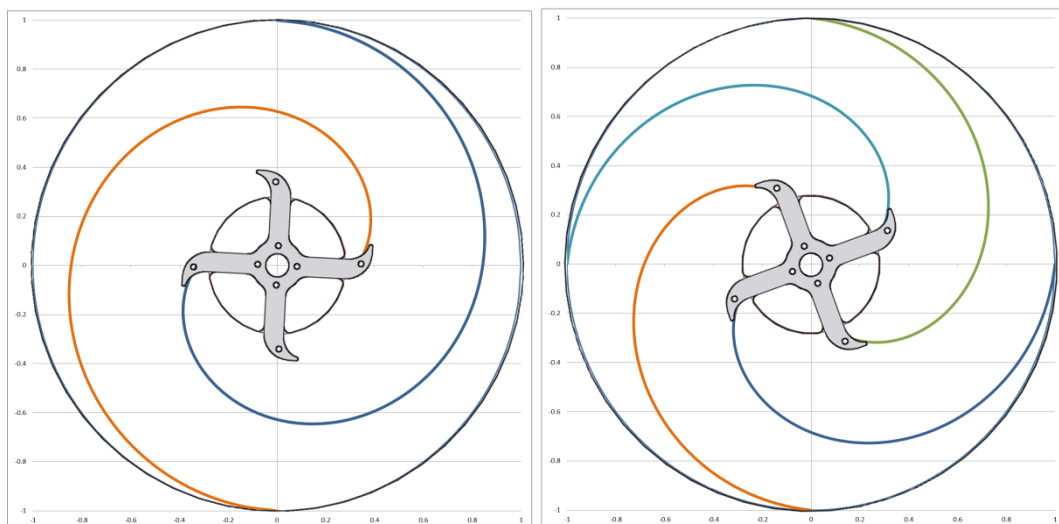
Rotorový disk (vlevo) a spojovací obrouč rotorových disků (vpravo)
